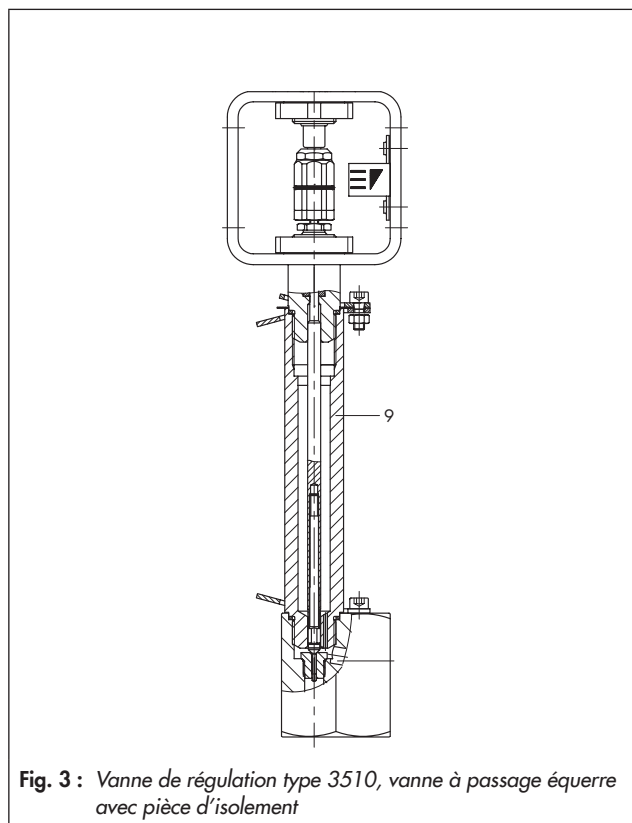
Vanne de régulation type 3510, vanne à passage équerre avec pièce d'isolement
